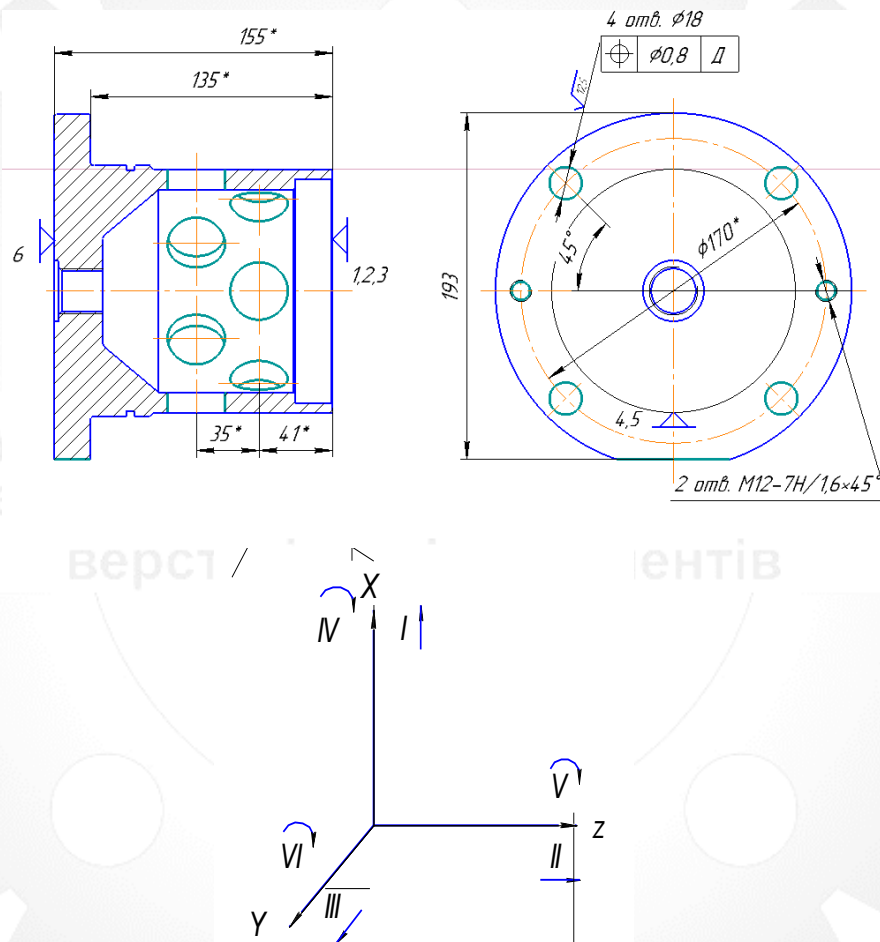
Схема базування на операції 040 Фрезерна
